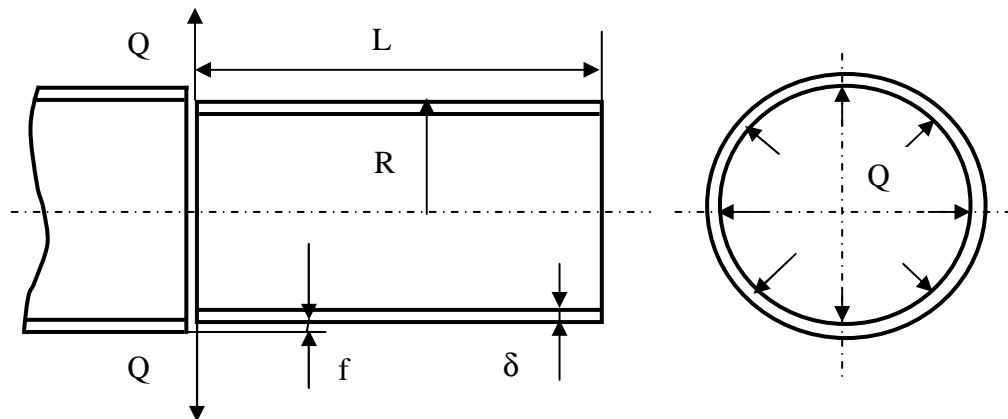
Розрахункова схема вигину кромки обичайки внутрішнім центратором
